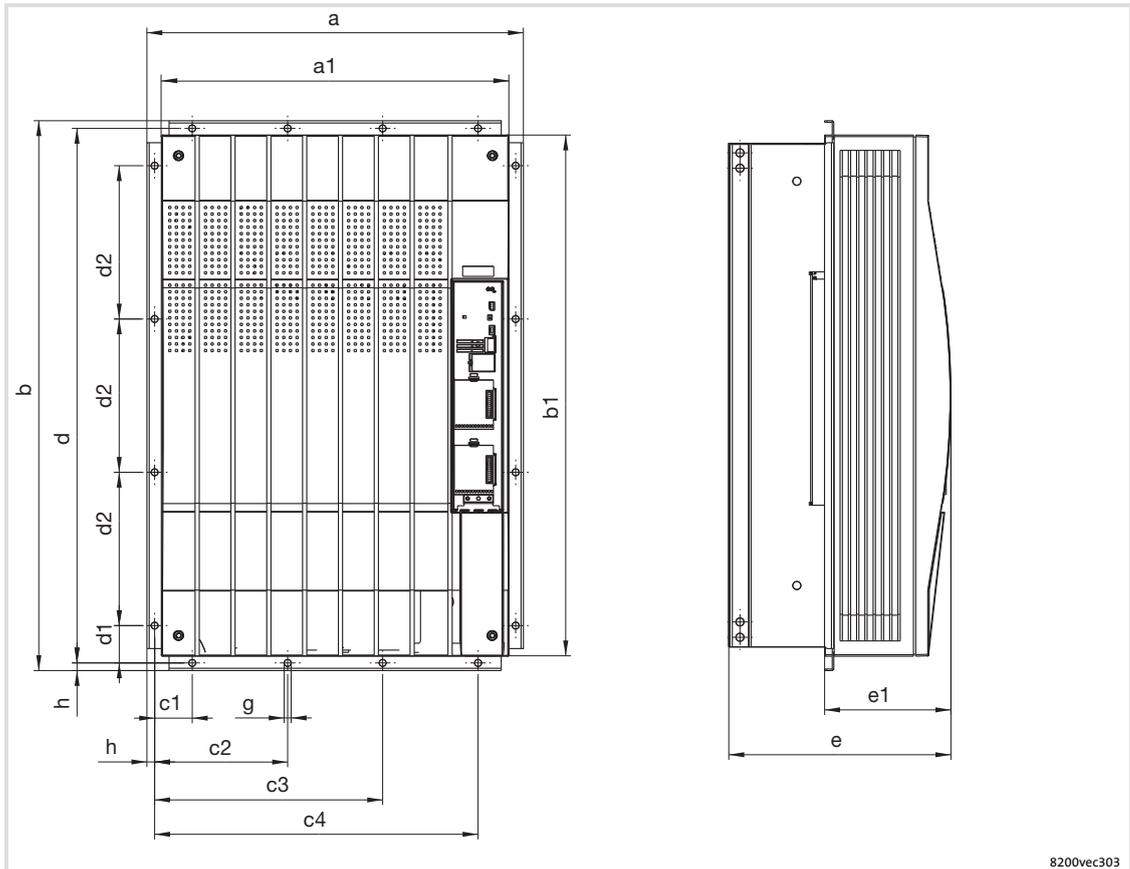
Abmessungen Montage thermisch separiert 75 ... 90 kW
